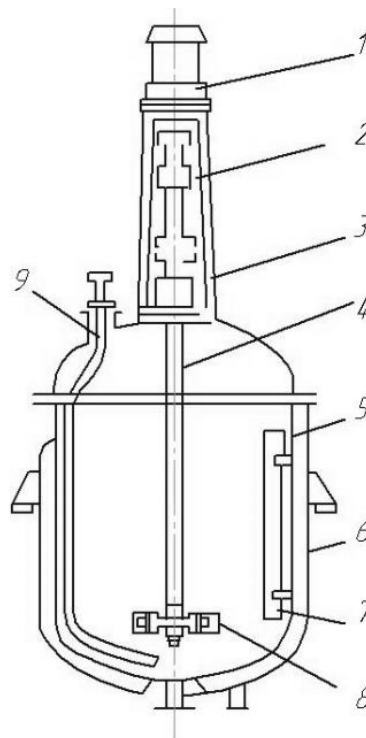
Змішувач з пристроєм, що перемішує: 1 - привід; 2 – стійка приводу; 3 – ущільнення; 4 – вал; 5 – корпус; 6 – сорочка; 7 - відбивна перегородка; 8 – мішалка; 9 – труба
